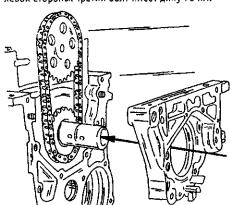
Установка передней крышки. Покрыть поверхность блока цилиндров уплотняющей массой.
